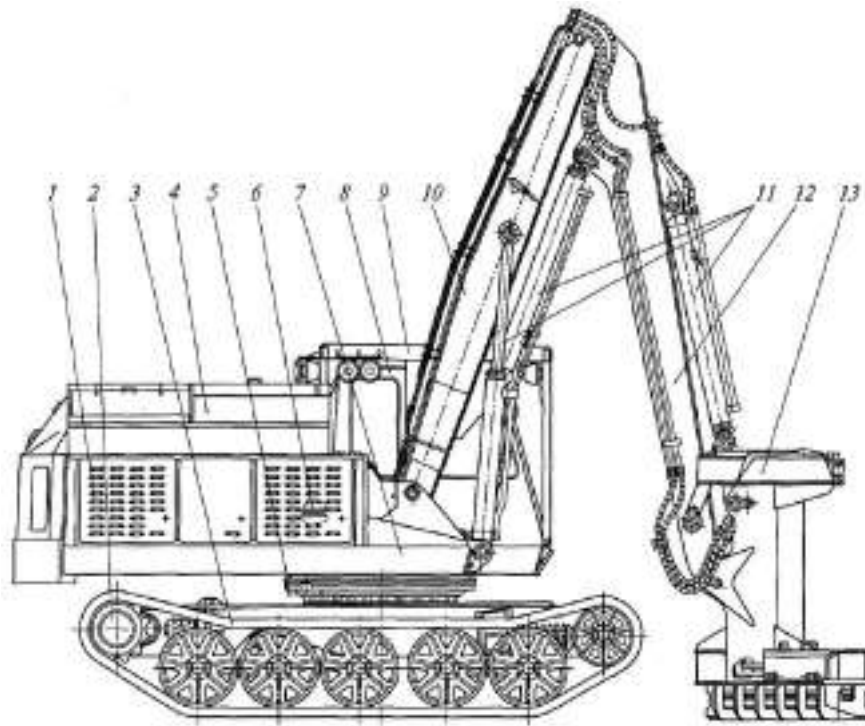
Валочно-пакетирующая машина МЛ-119А:
